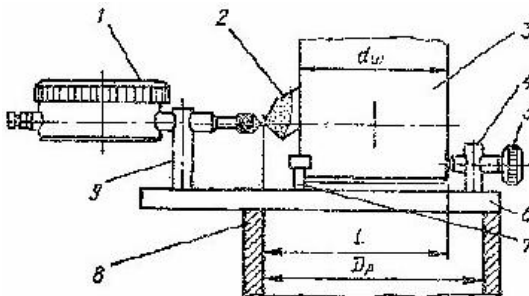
Індикаторний пристрій для встановлення вильоту різця:
